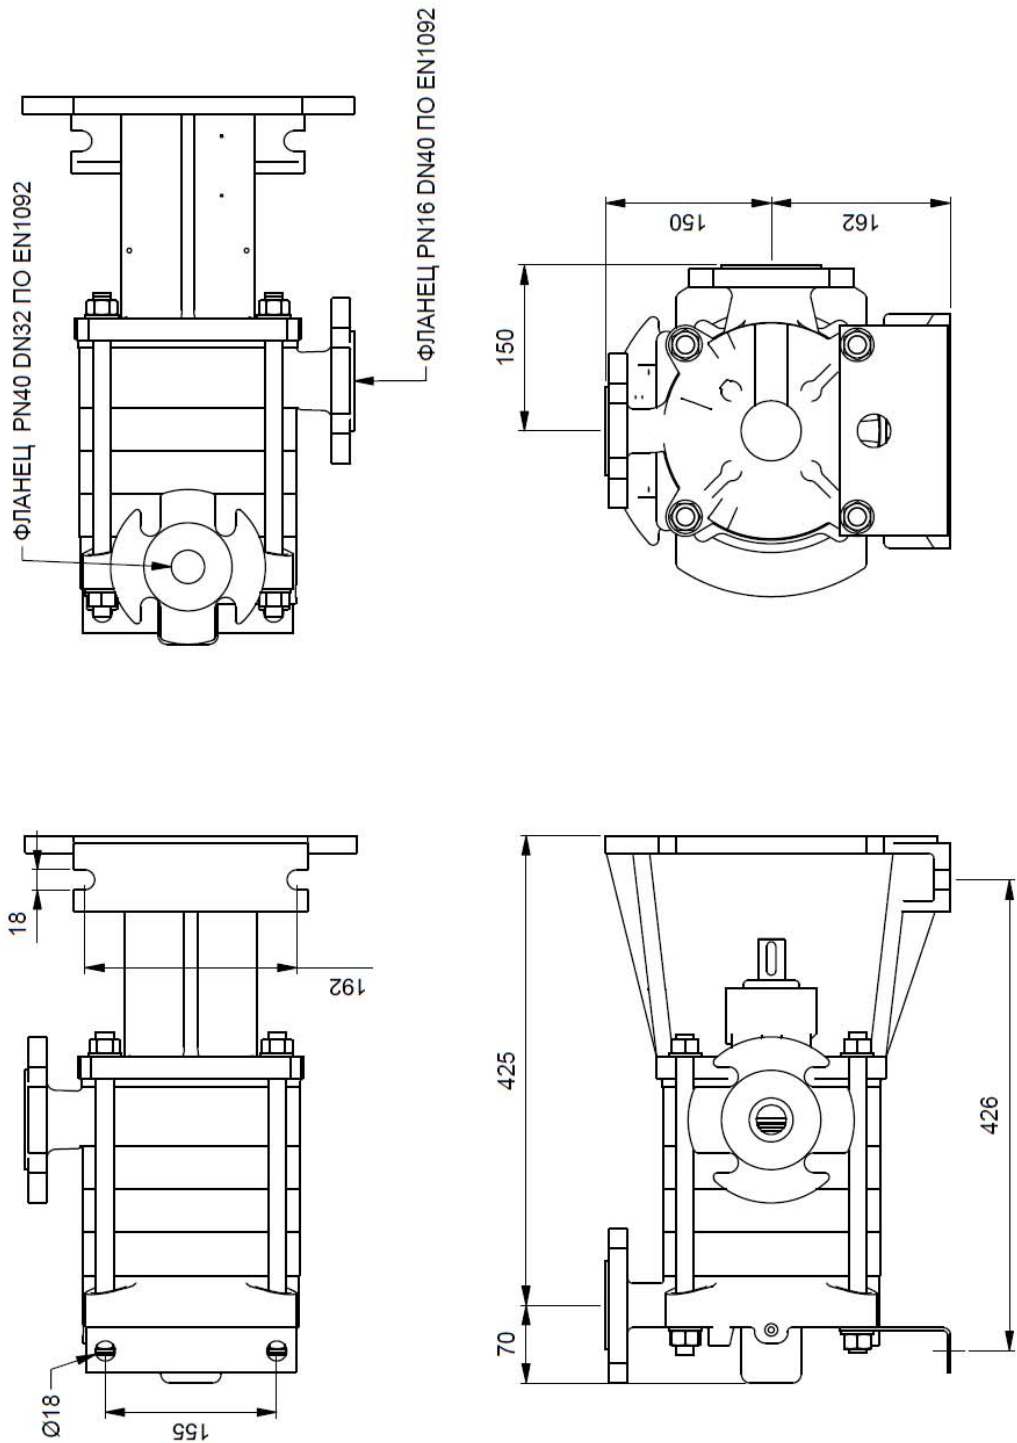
Габаритный чертеж насоса TSL 32/4 и присоединительные размеры
